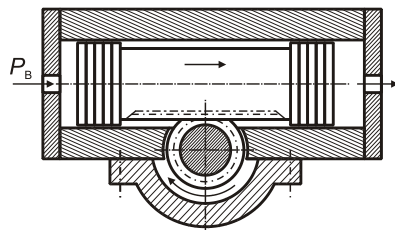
Поворотный пневмоцилиндр ($P_{в}$ — давление воздуха)
